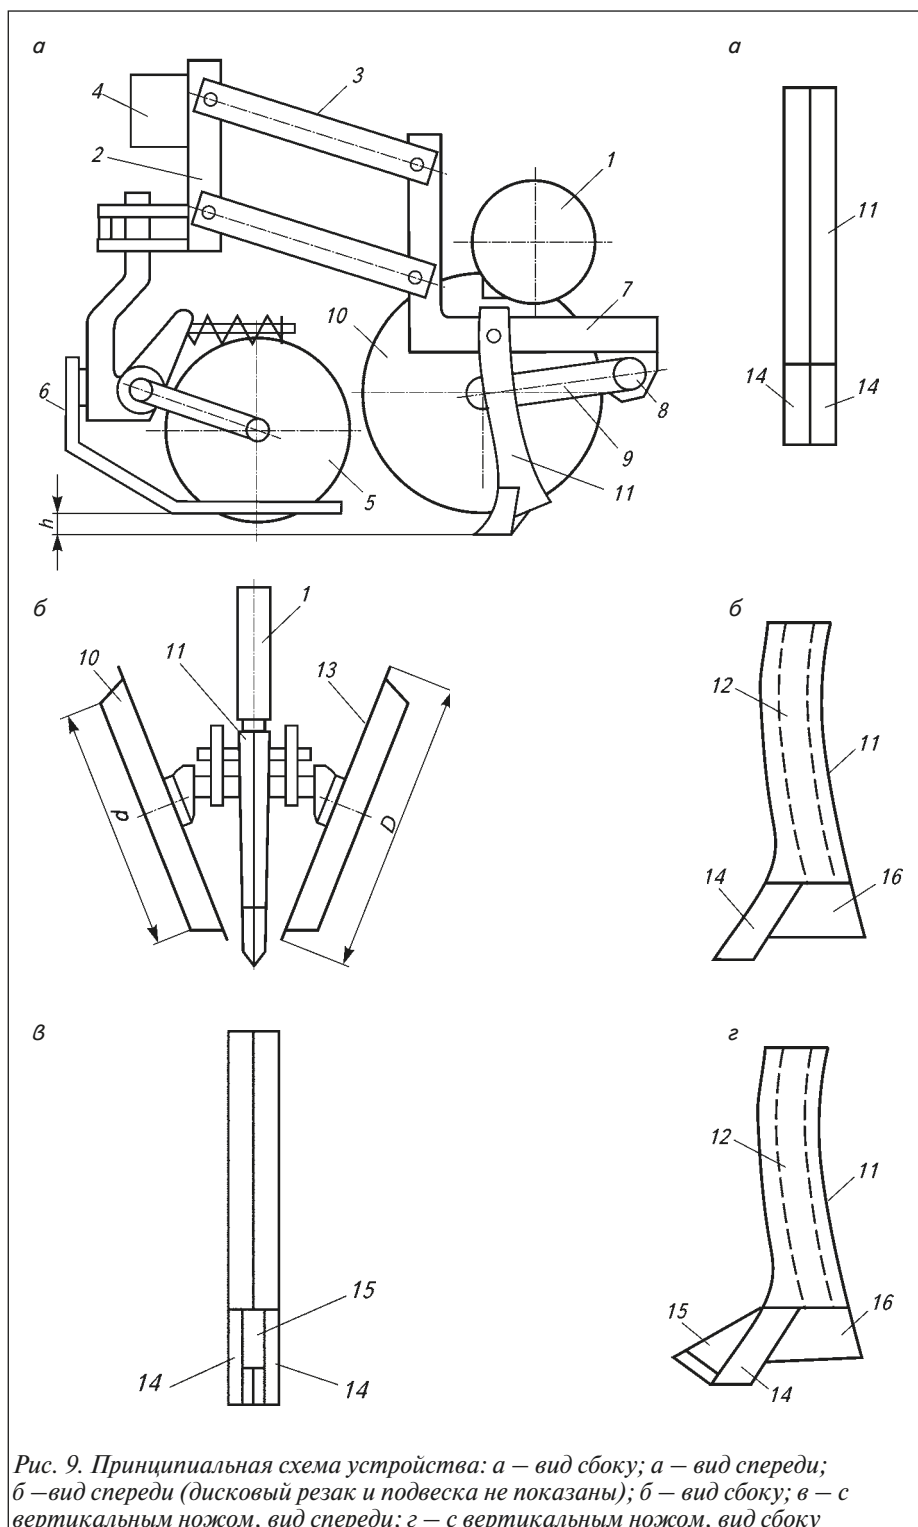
Принципиальная схема устройства: а – вид сбоку; а – вид спереди; б – вид спереди (дисковый резак и подвеска не показаны); б – вид сбоку; в – с вертикальным ножом, вид спереди; з – с вертикальным ножом, вид сбоку
